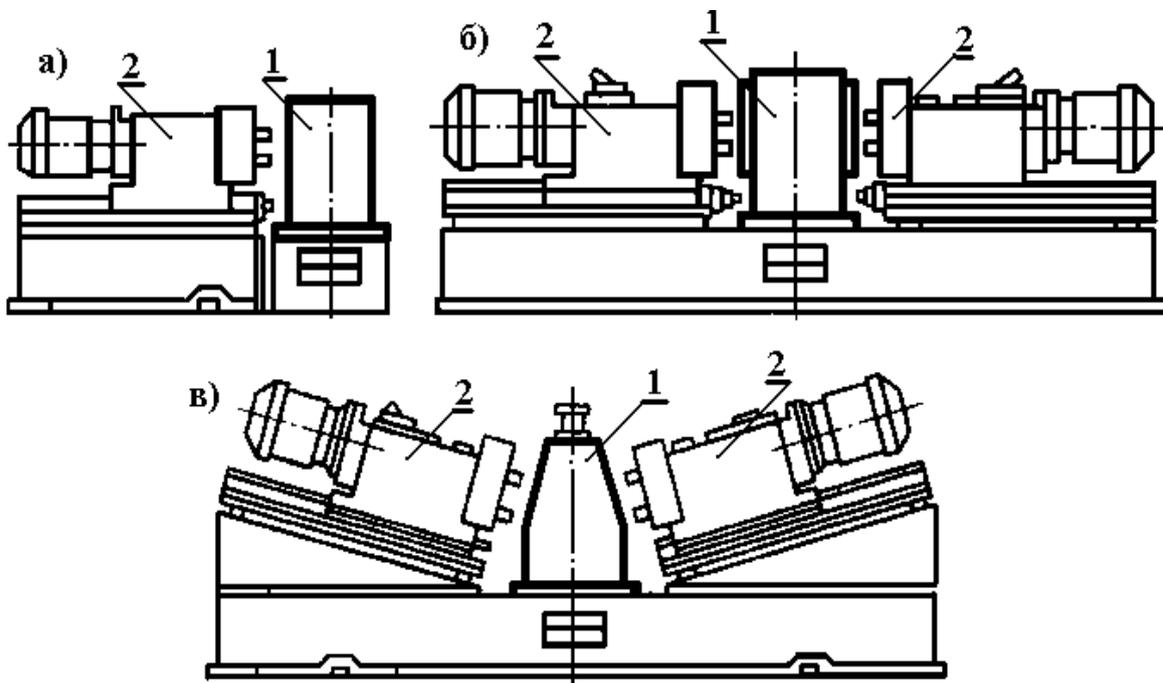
Силовые головки. 1- заготовка, 2- силовая головка.
